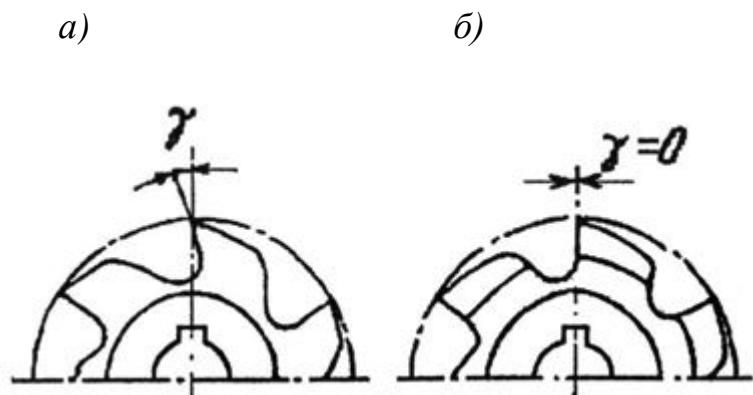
Форма зуба фрезы: а – острый зуб;
